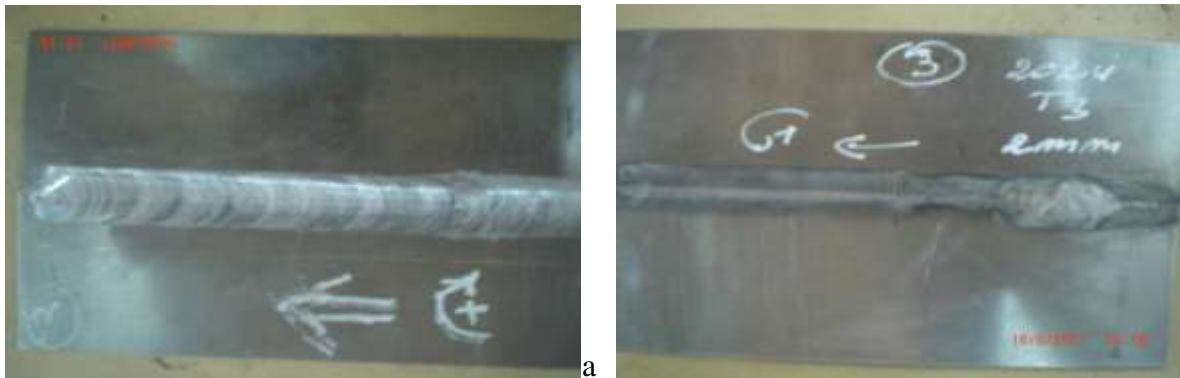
Soudage de la tôle 2024-T3 ($e = 3 \text{ mm}$), $V_r = 1500 \text{ tr/min}$, $V_a = 36 \text{ mm/min}$, $\alpha = 2^\circ$ a) face avant et b) faces arrière
